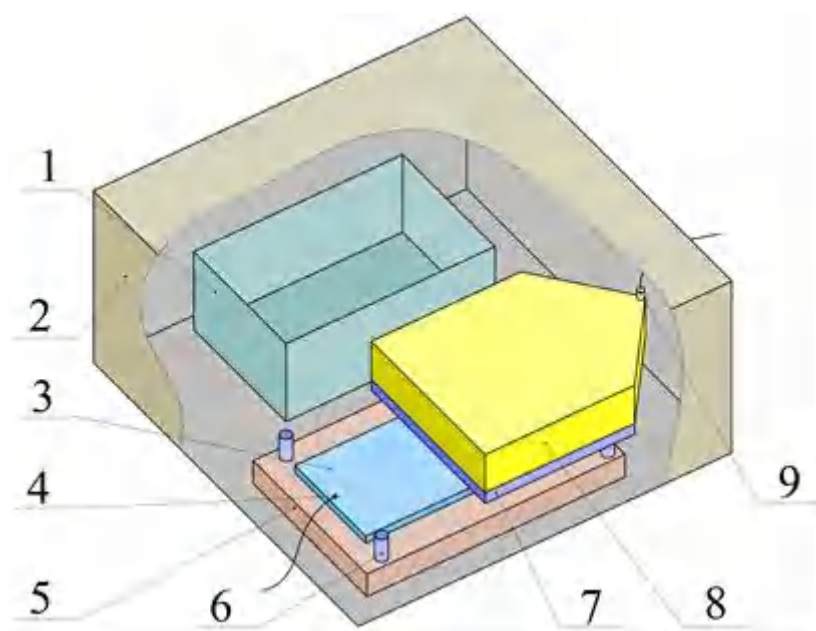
Схема сварки с охлаждением неподвижной пластины (метаемая пластина и заряд условно рассечены): 1 – ёмкость с жидким азотом; 2 – закрытый контейнер; 3 – неподвижная пластина; 4 – термопара; 5 – основание; 6 – сварочный зазор; 7 – метаемая пластина; 8 – заряд ВВ; 9 – детонатор
